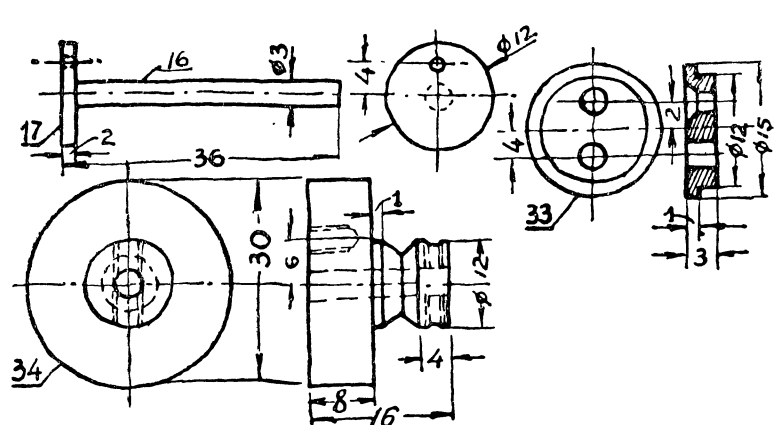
Размеры маховика и эксцентрика (для изготовления на токарном станке)
